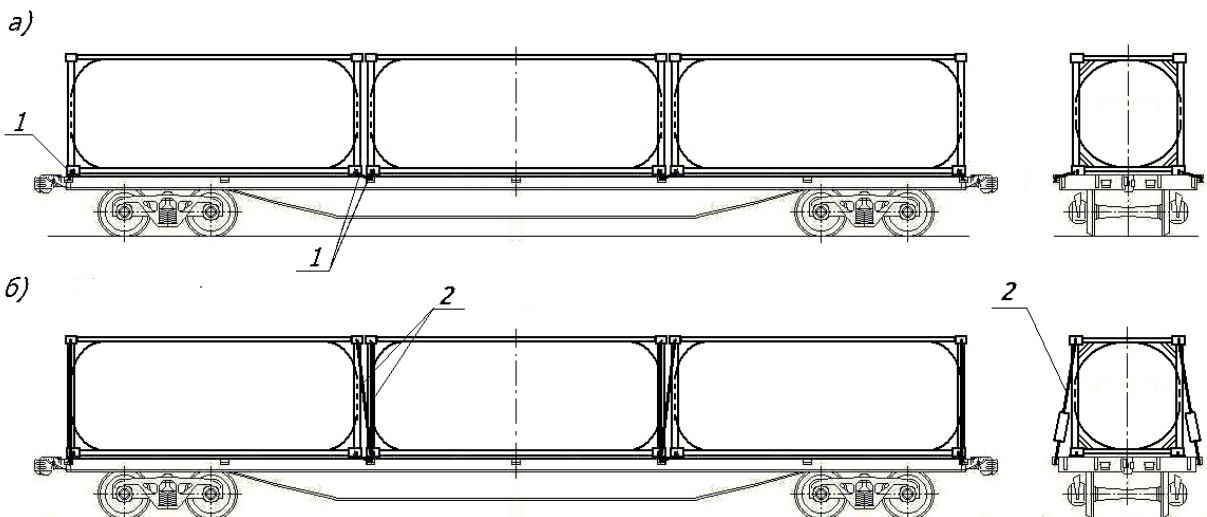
Дополнительное крепление контейнеров-цистерн на платформе для крупнотоннажных контейнеров:
